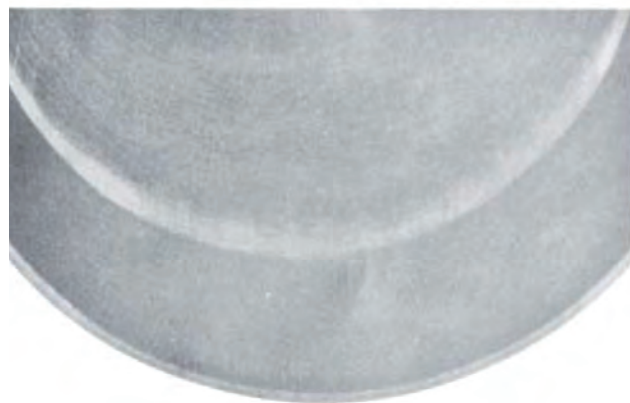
Ligne brillante tout autour de l'alésage du cylindre
